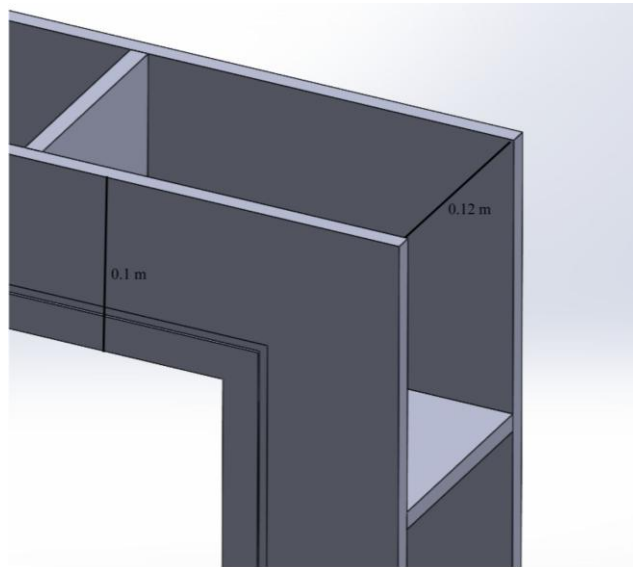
ESQUINA DEL MARCO CON RANURA DE O-RING.
